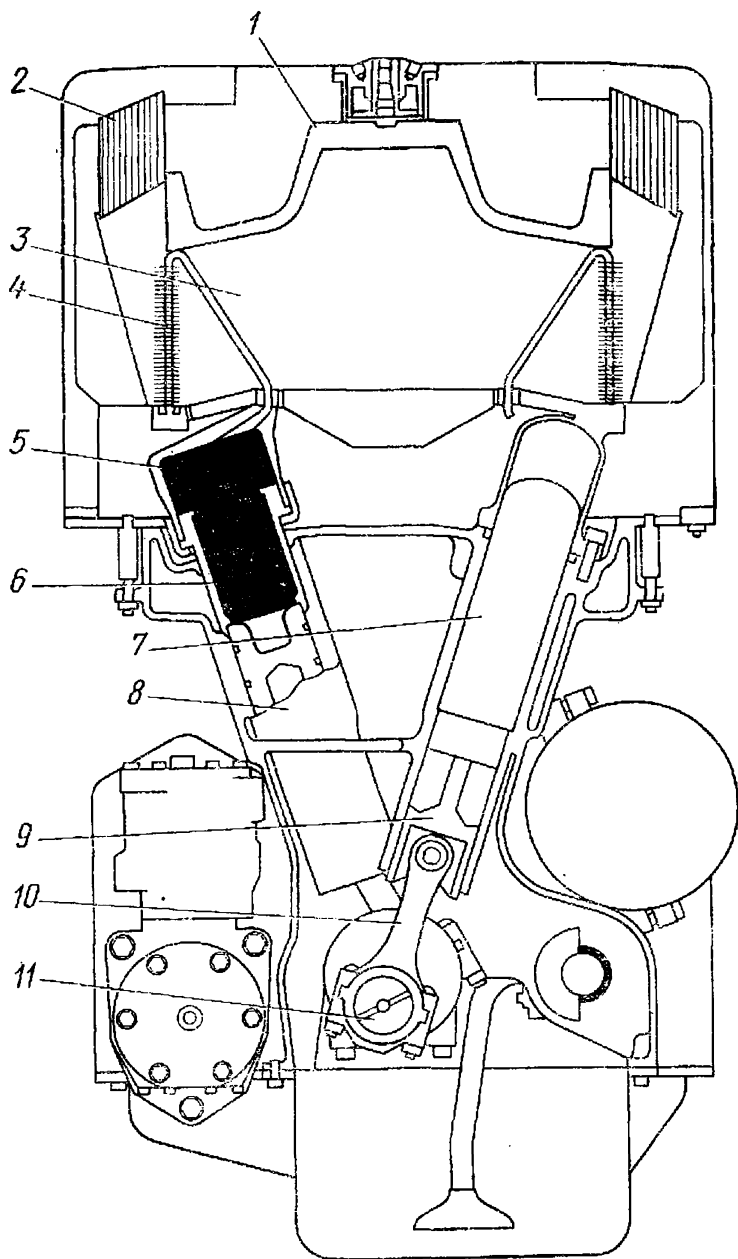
Поперечный разрез двигателя Стирлинга двойного действия типа P150 фирмы «Юнайтед Стирлинг» [289]:
